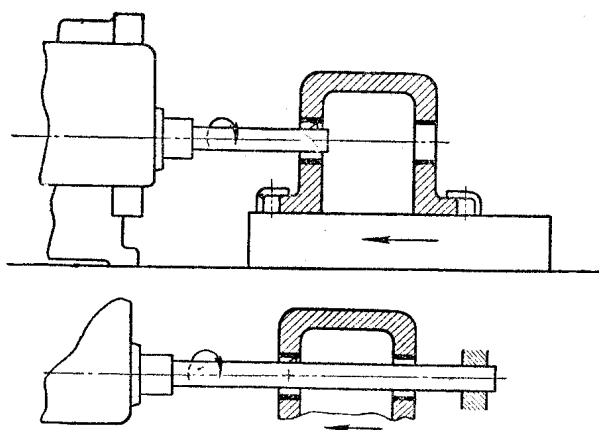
Схема розточування отворів без кондуктора з подачею столу
